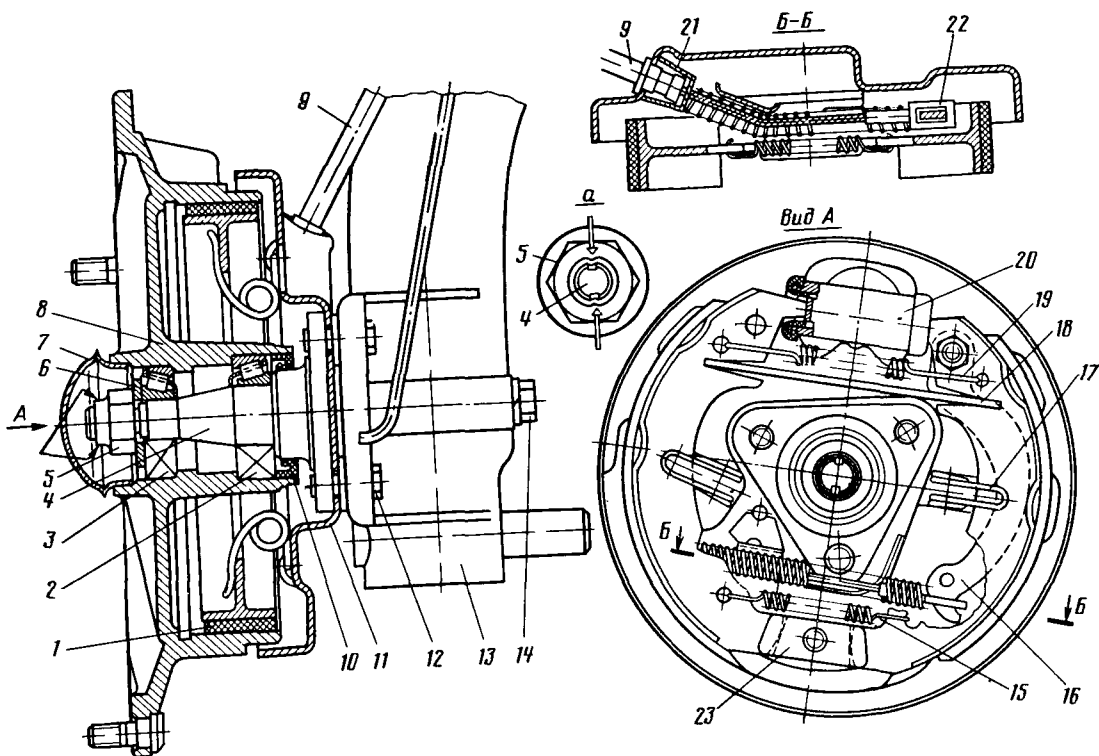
Задняя подвеска и задний тормоз со ступицей и подшипниками:
